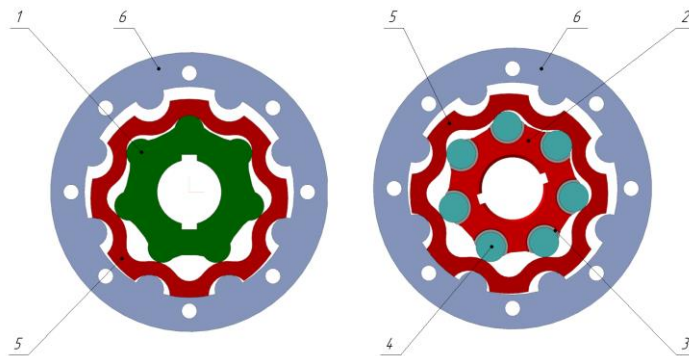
Конструкції передач: 1- цільний ротор; 2- збірний ротор; 3- підшипник металополімерний; 4- цівка збірного ротора; 5- корінний статор; 6- статор
